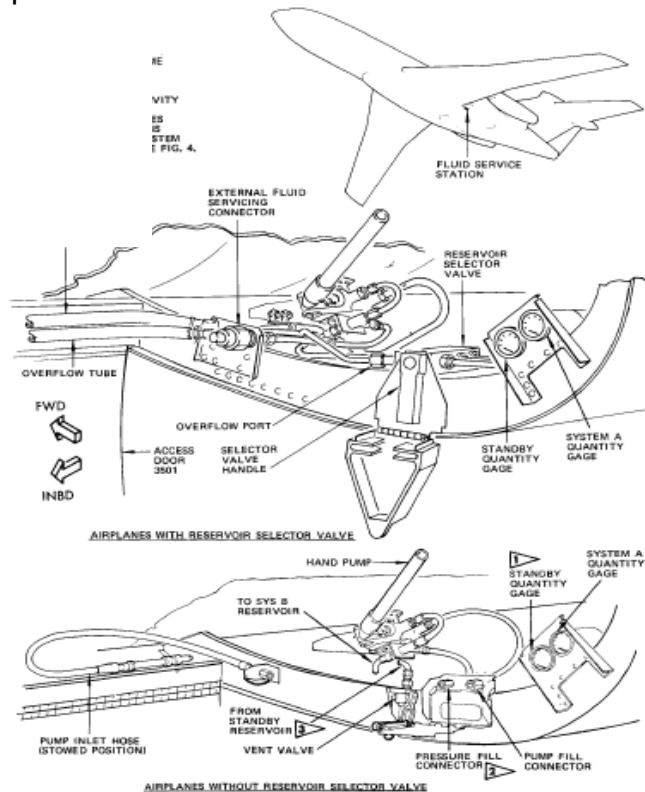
Localización del equipo de llenado (Fuente: B727-AMM)
